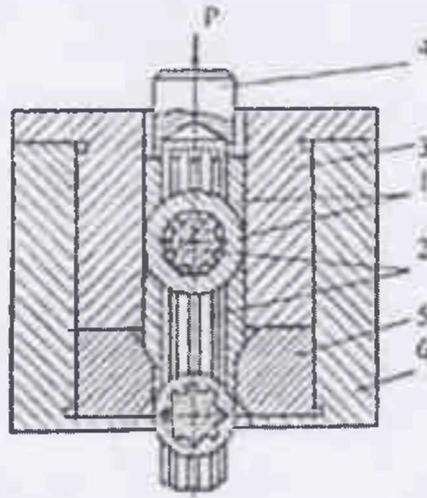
Схема процесу формоутворення внутрішніх шліців в трубних заготовках
